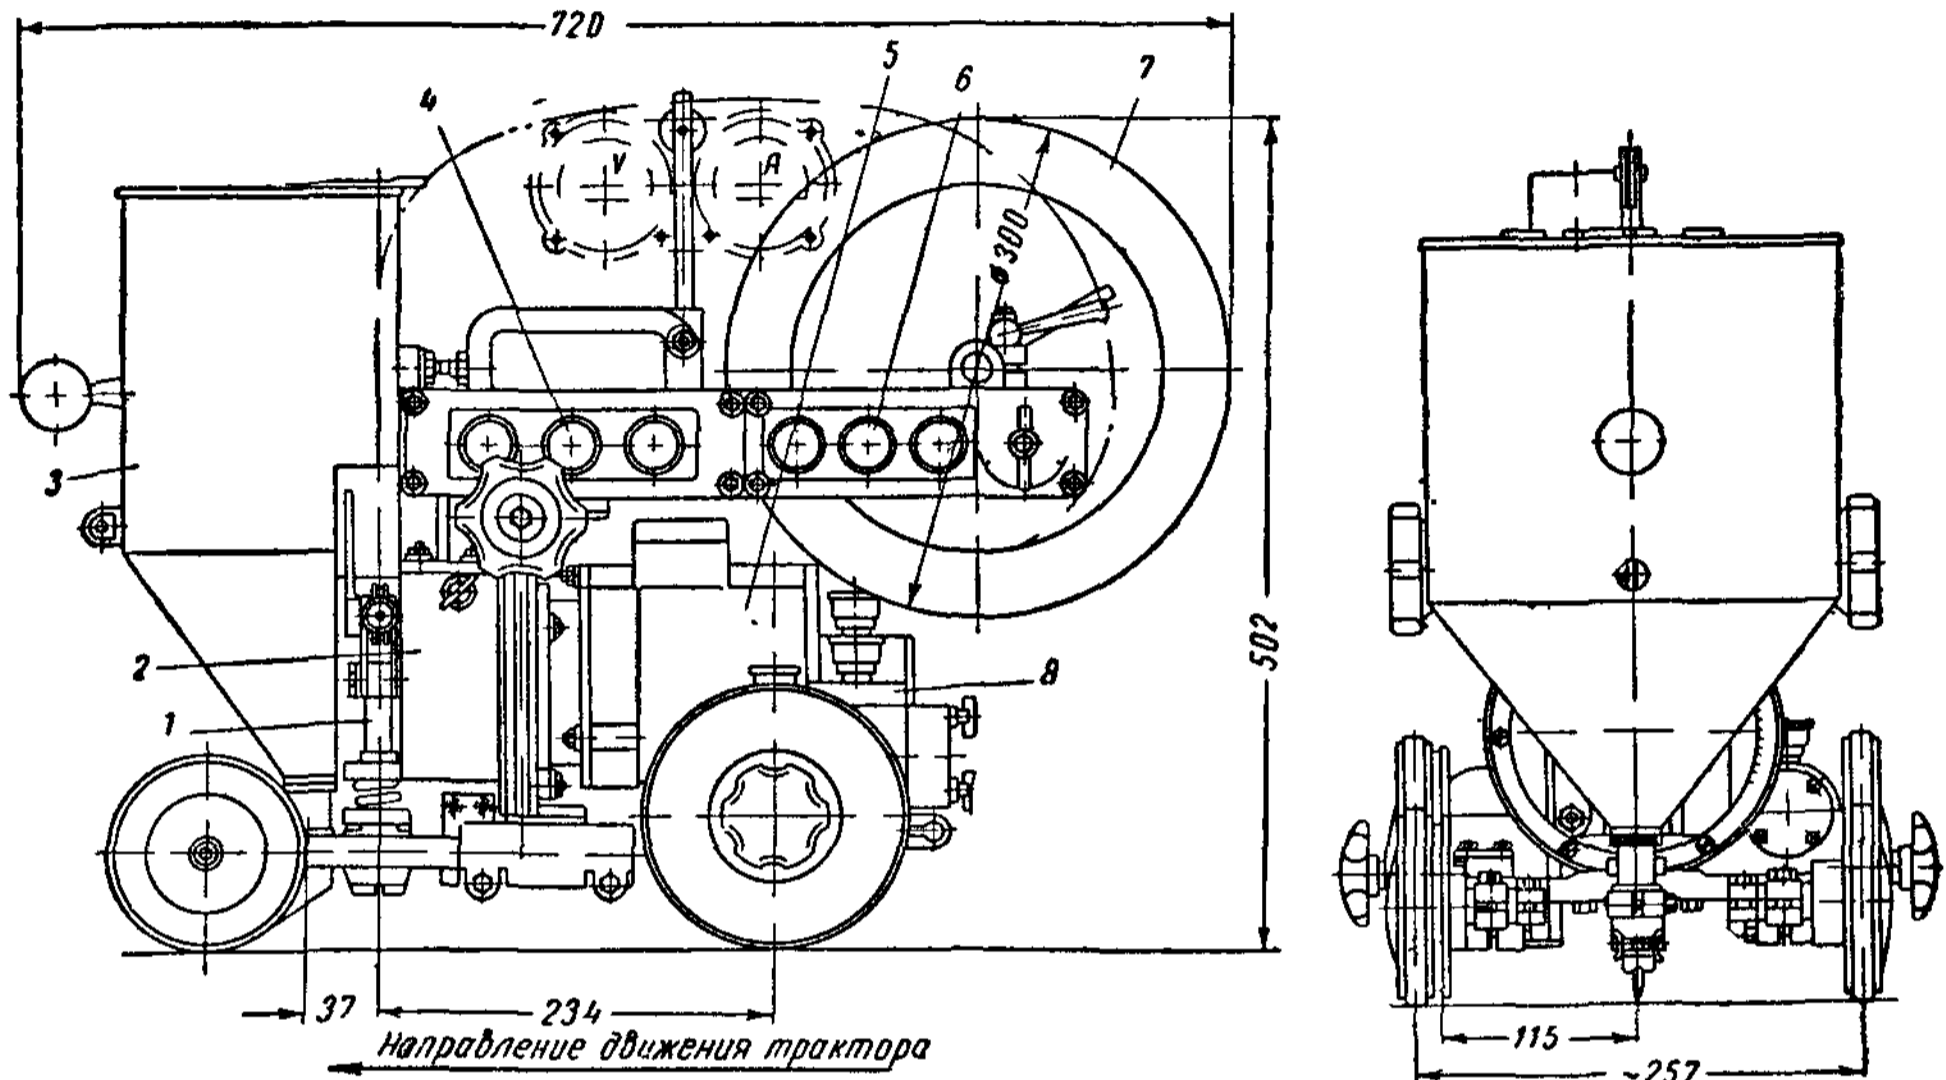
Сварочный трактор типа ТС-17М (схема)
